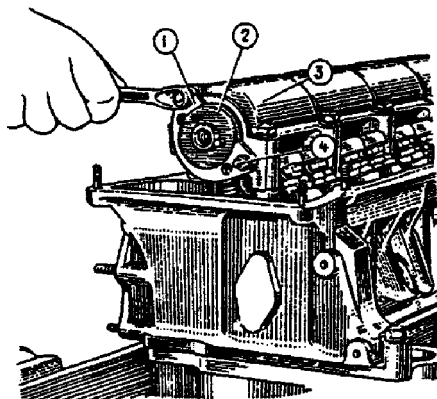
Desmontagem do flange da extremidade da árvore de comando das válvulas: 1 - flange; 2 - árvore de comando das válvulas; 3 - corpo dos casquilhos; 4 - porcas de fixação do flange.
